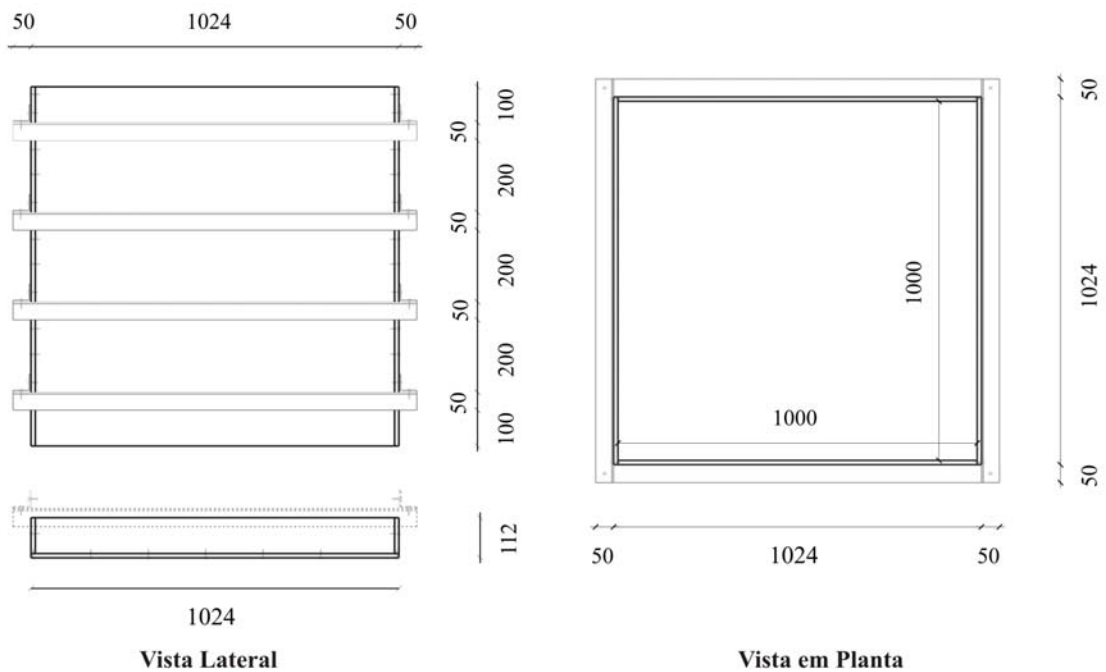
Vistas lateral e em planta do lisímetro com suas dimensões (mm)
